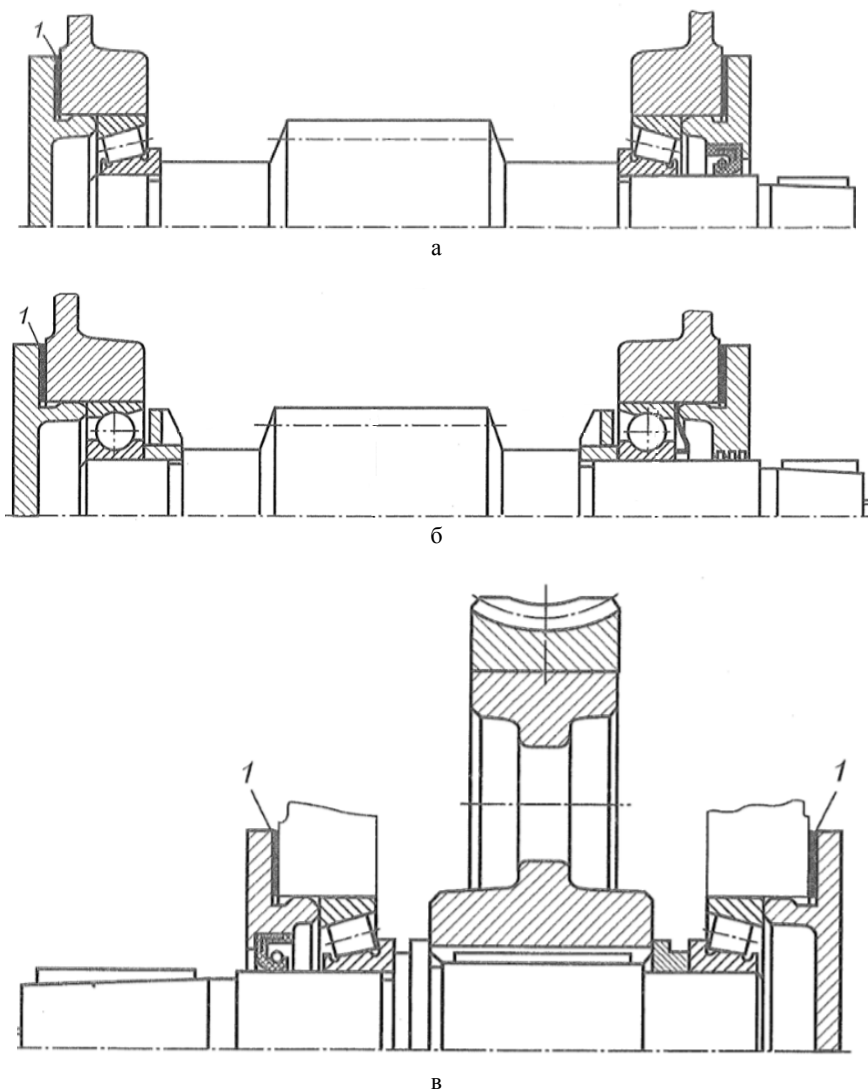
Установка «впаспор» вала: а, б – червяка (1 – набор металлических регулировочных прокладок для регулировки зазора в подшипниках); в – червячного колеса (1 – набор металлических регулировочных прокладок для регулировки зазора в подшипниках и регулировки зацепления в передаче)
